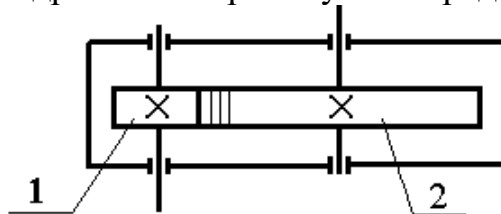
Схема цилиндрической прямозубой передачи:
